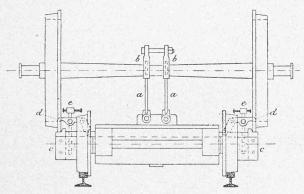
Truc-transporteur de la Fabrique d'Esslingen. Vue de bout.
